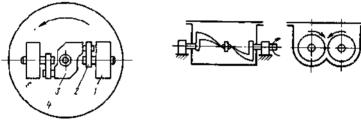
Схемы бегунов с вращаю- Рис. 1.29. Схема смесителя с щимися катками: 1 - каток; 2 - серьга; z-образными лопастями 3 - ведущая траверса; 4 - чаша (стрелкой показано вращение катков)
